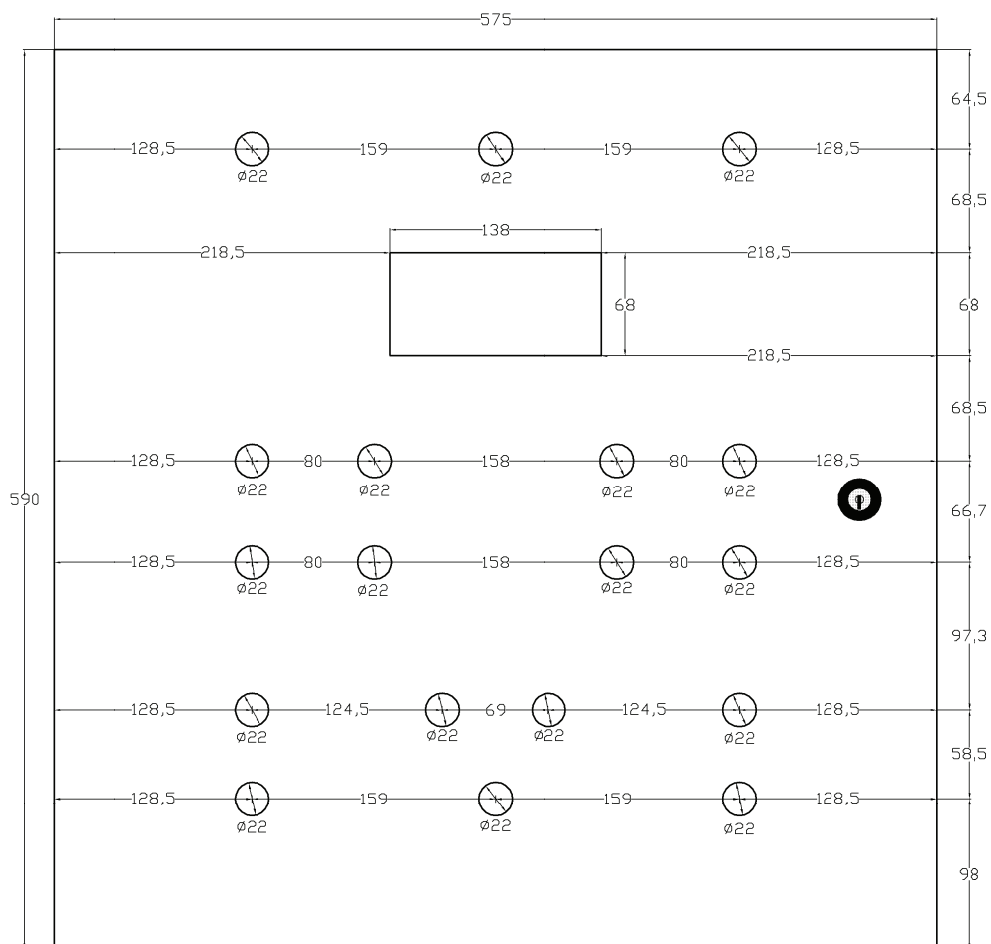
Medidas en milímetros para corte del panel frontal del tablero de mando
